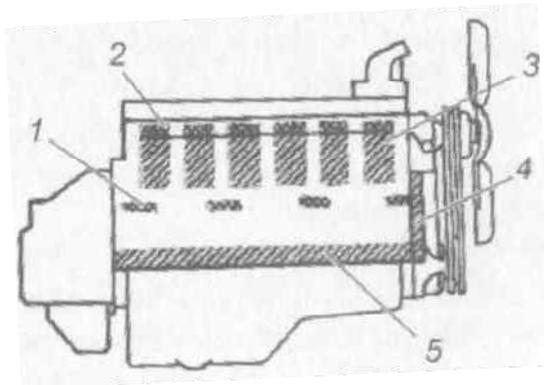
Зоны прослушивания двигателя для определения дефектов различных деталей: 1 – клапанов; 2 – поршневых пальцев, шатунных подшипников; 3 – Распределительных зубчатых колец; 4 – коренных подшипников; 5 - подшипников распределительного вала.
